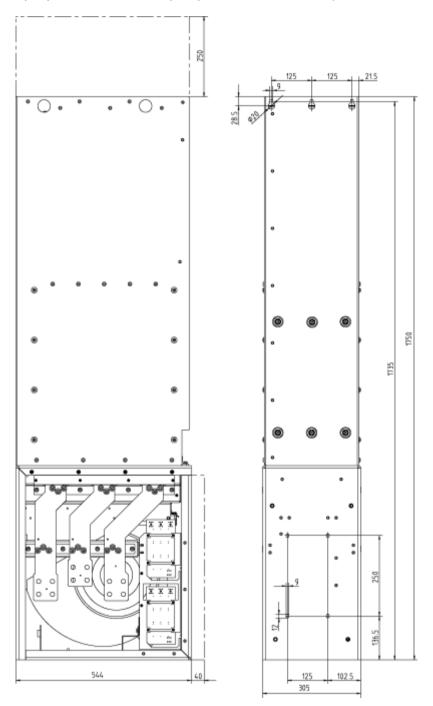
Габаритный чертеж активного интерфейсного модуля, типоразмер HI. Вид сбоку, вид сзади
